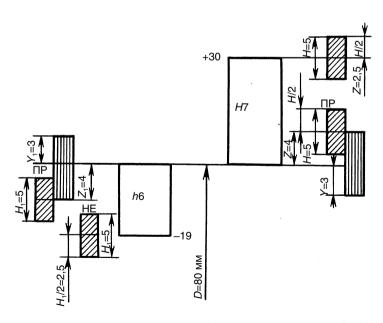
Схема расположения полей допусков калибров для контроля деталей Ø80H7/h6
